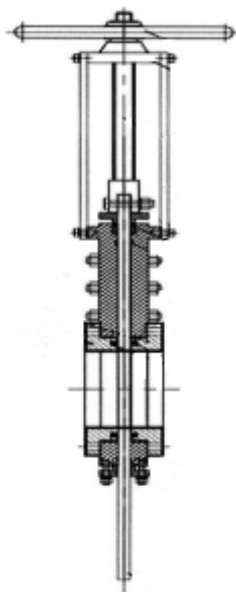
Общий вид шиберной задвижки конструкции
